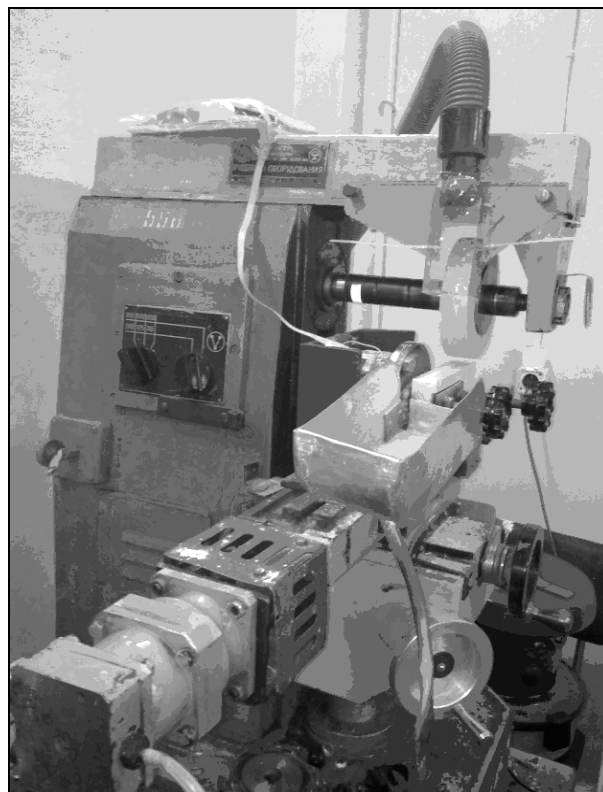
Лабораторная установка на базе горизонтально-фрезерного станка НГФ-110Ш4
